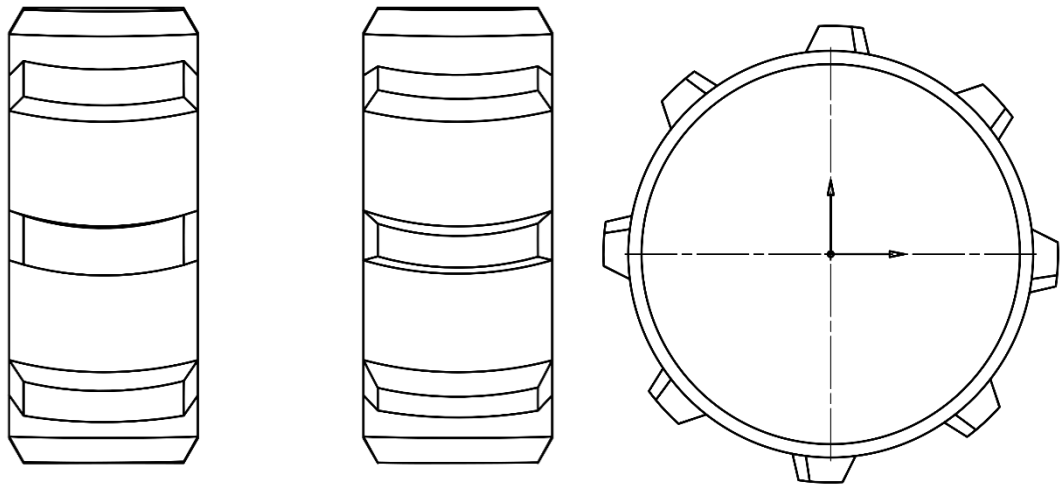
Профили лопастей колеса центратора 4 (слева) и 5 (центр);
